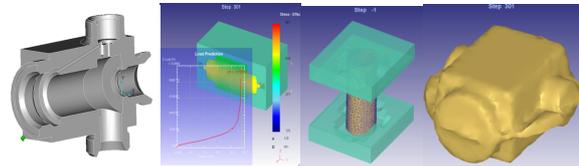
Модель детали, анализ процесса прессования, модель заготовки
